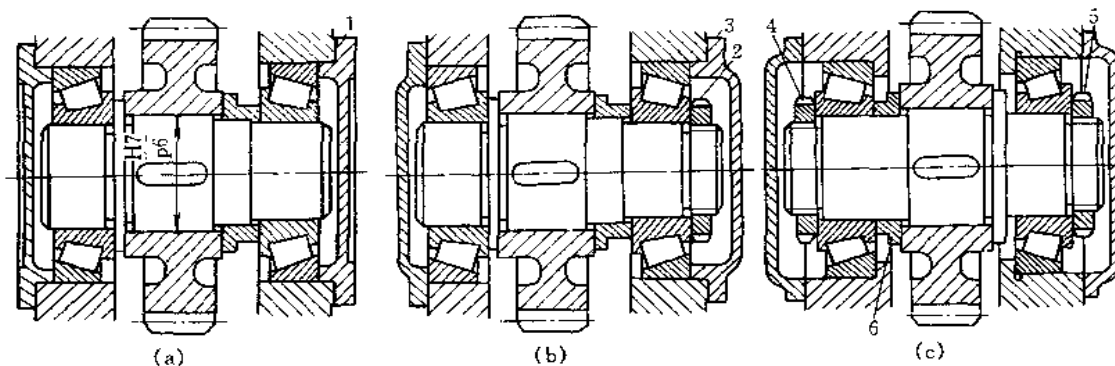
齿轮传动成对圆锥滚子轴承的配置与固定
